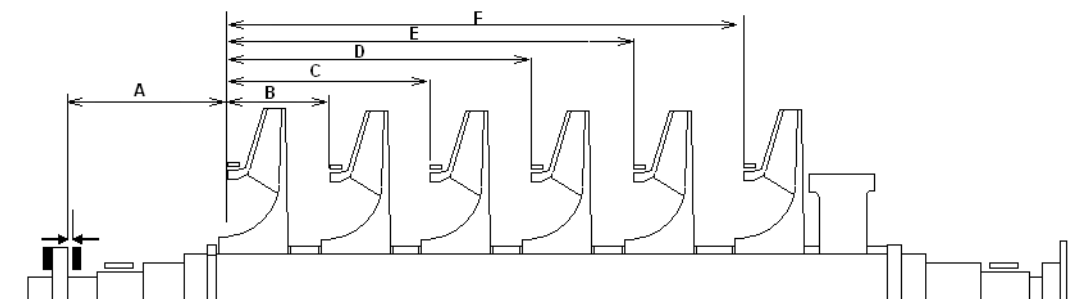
Levantamento dimensional axial (NOBREGA,2005)
